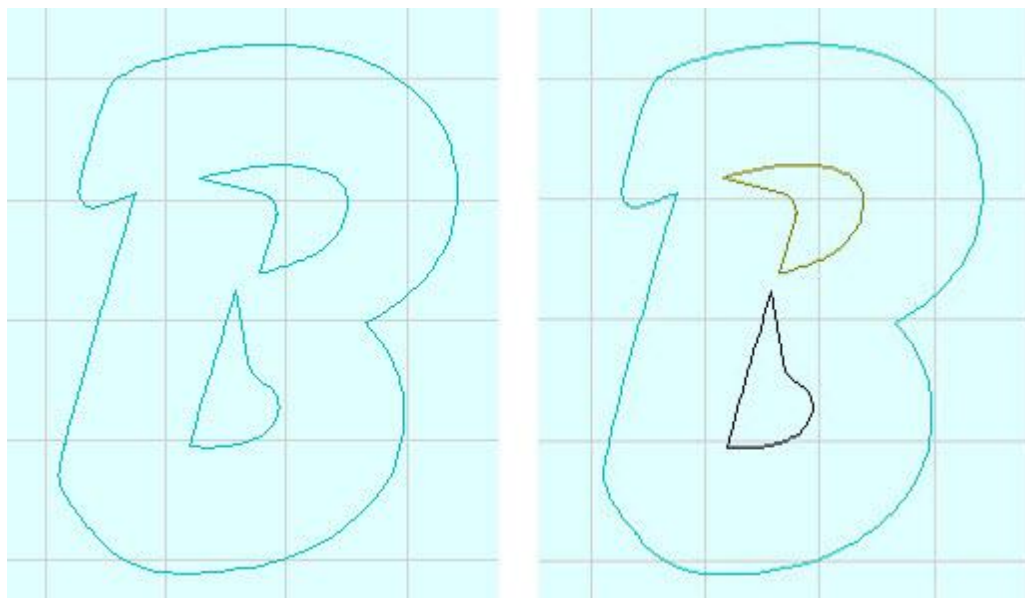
Links nur ein Werkzeug, rechts mehrere Werkzeuge (farblich gekennzeichnet)
